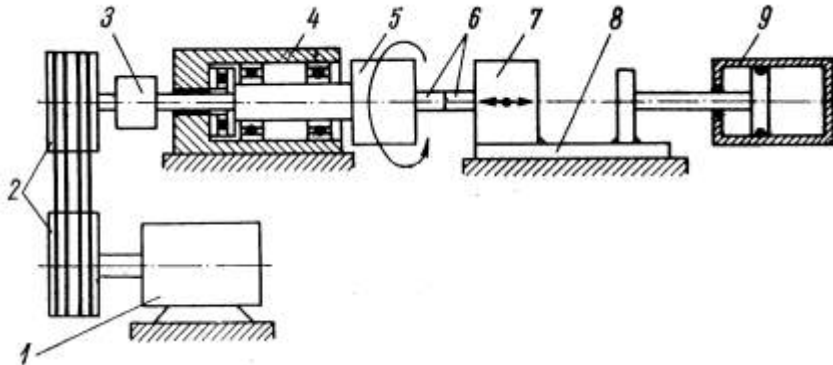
Принципова конструктивна-кінематична схема установка СТ110 для зварювання тертям:
